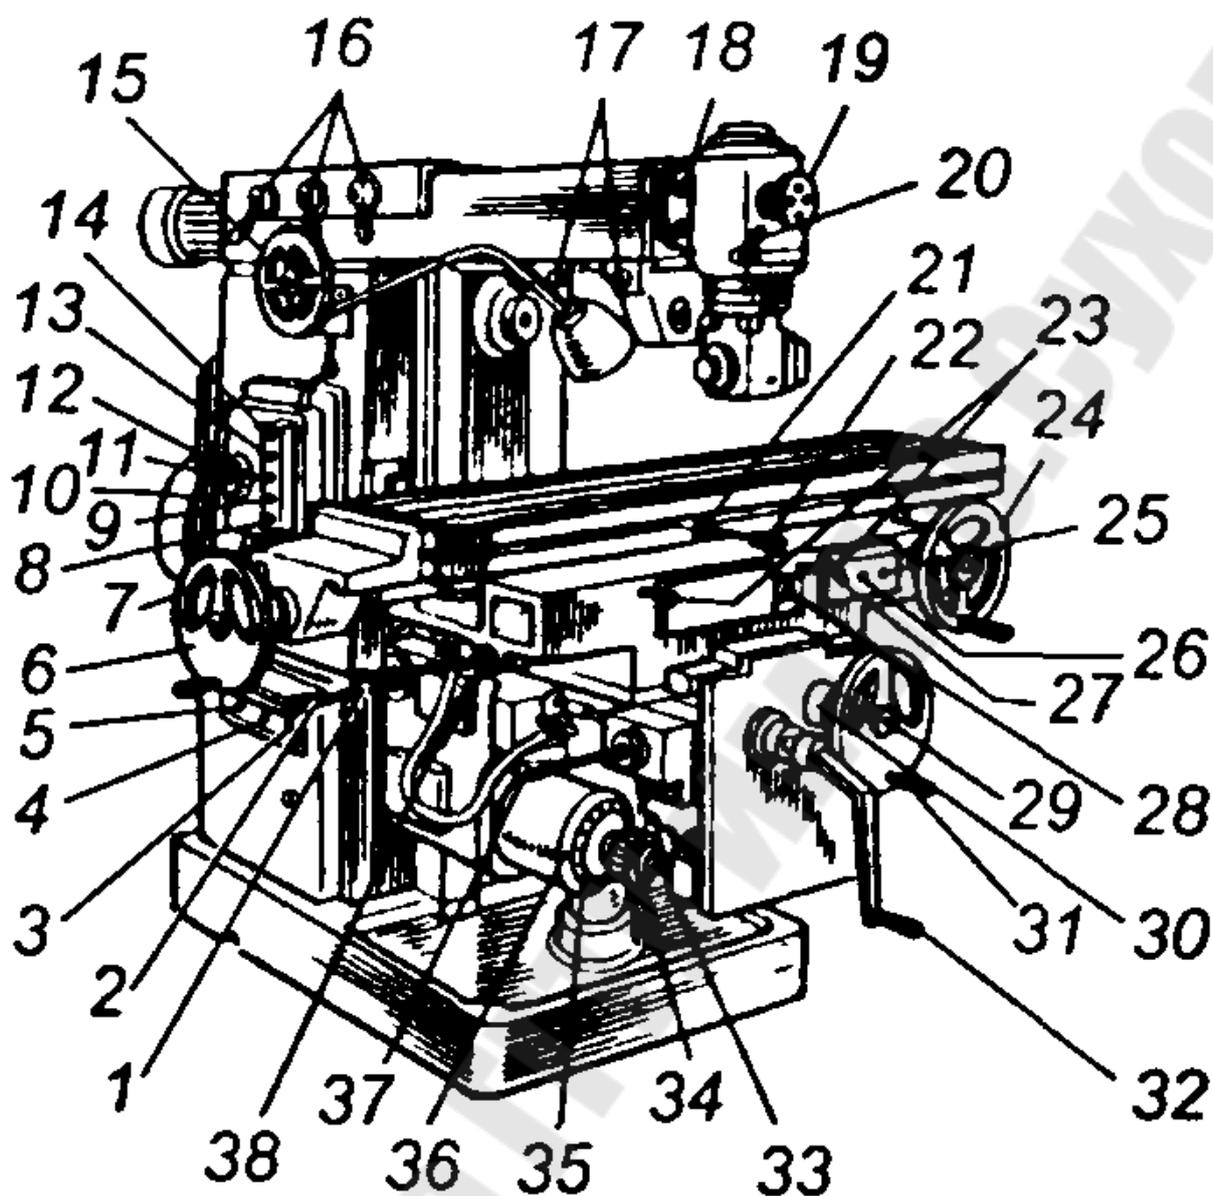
Общий вид широкоуниверсального консольного фрезерного станка: 1 – рукоятка включения продольных перемещений стола; 2, 37 — рукоятки включения поперечной и вертикальной подач стола; 3 — переключатель ввода «Включено—выключено»; 4 — переключатель насоса охлаждения «Включено—выключено»; 5 — переключатель вращения горизонтального шпинделя «Влево—вправо»; 6, 24 – маховички ручного продольного, перемещения стола; 7— рукоятка переключения скоростей горизонтального шпинделя; 8, 27— кнопка «Стоп»; 9, 26 – кнопка «Пуск шпинделя»; 10 – стрелка указателя частоты вращения шпинделя; 11 — указатель частоты вращения шпинделя; 12, 25 — кнопка «Быстро стоп»; 13 — кнопка «Импульс шпинделя»; 14 — переключатель освещения; 15 — маховичок ручного перемещения хобота; 16 — рукоятки переключения скоростей шпинделя поворотной головки; 17 — механизм зажима серьги; 18 — механизм зажима поворотной головки; 19 — маховичок выдвижения
